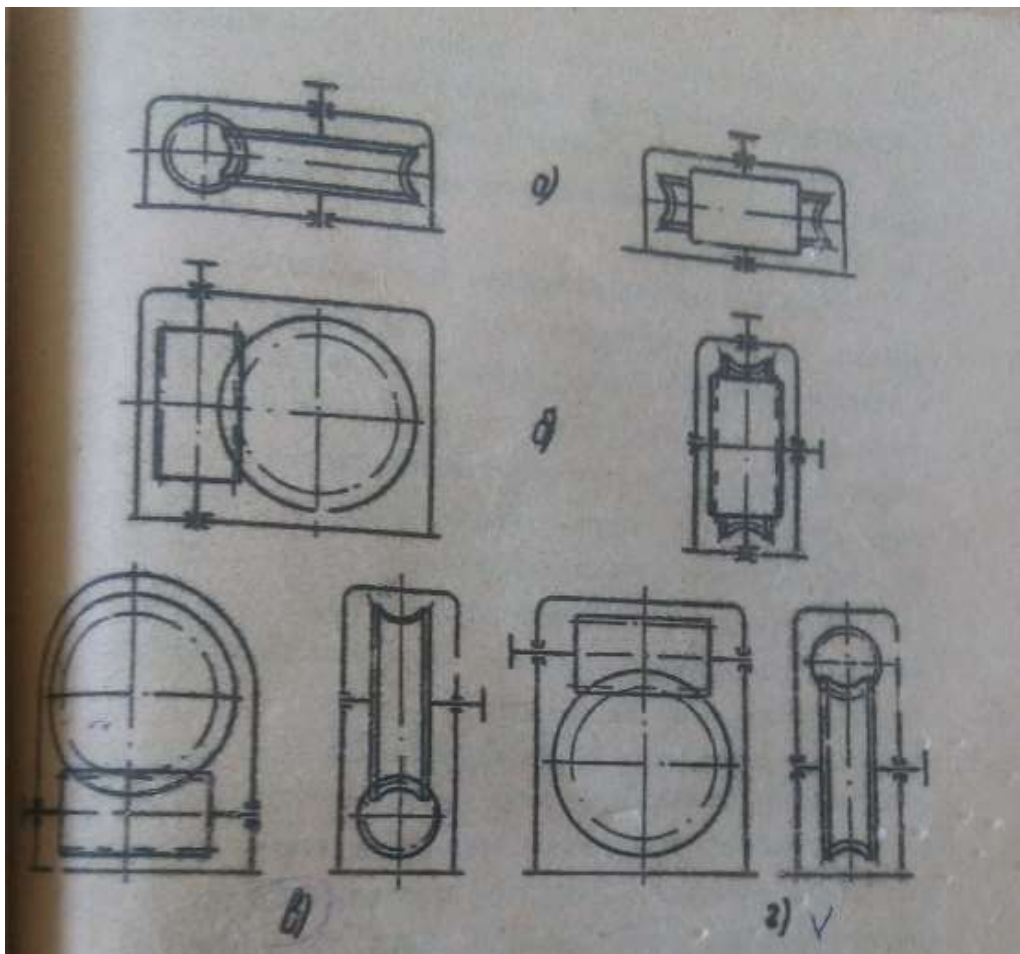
Кинематические схемы червячных и зубчато-червячных редукторов
